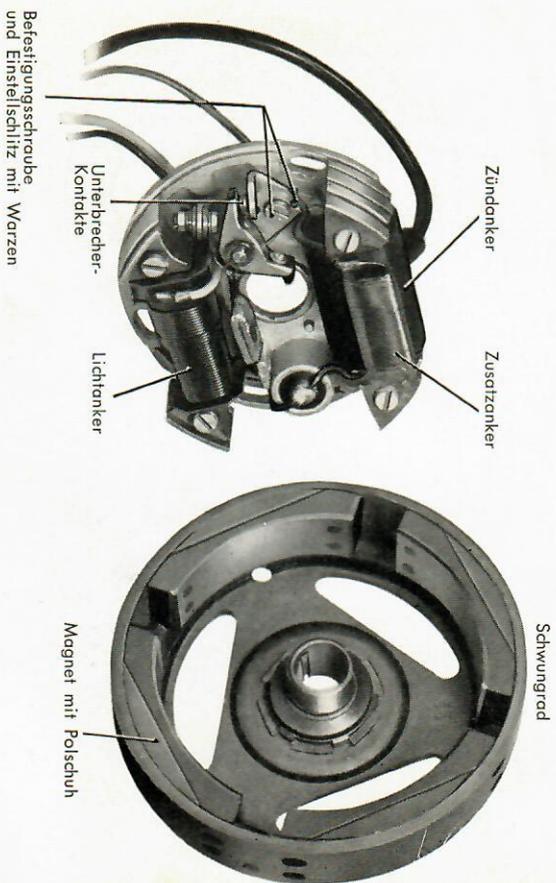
Bosch-Schwunglichtmagnetzünder LM/URC 1/116/29/5... mit Zusatzanker für Batterieladung oder Wechselstromhorn oder Bremslicht.
